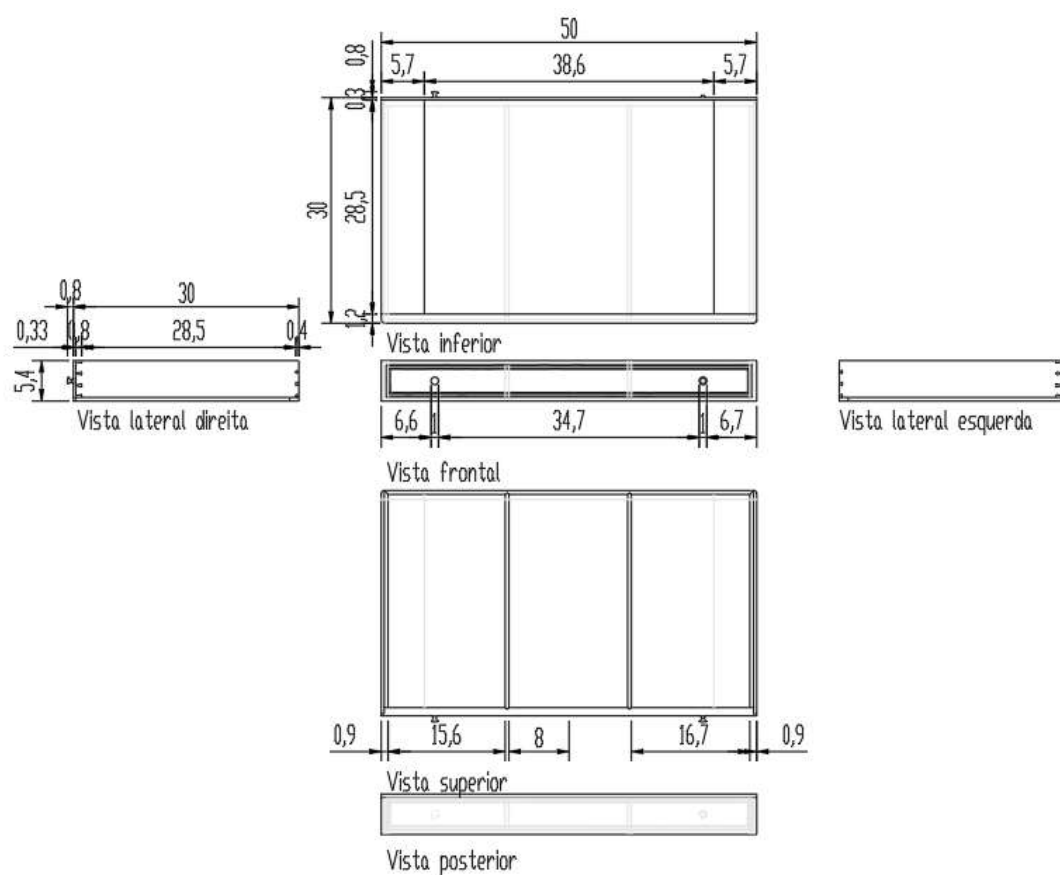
Dimensões gerais da primeira gaveta, em centímetros. Desenho técnico sem escala.
